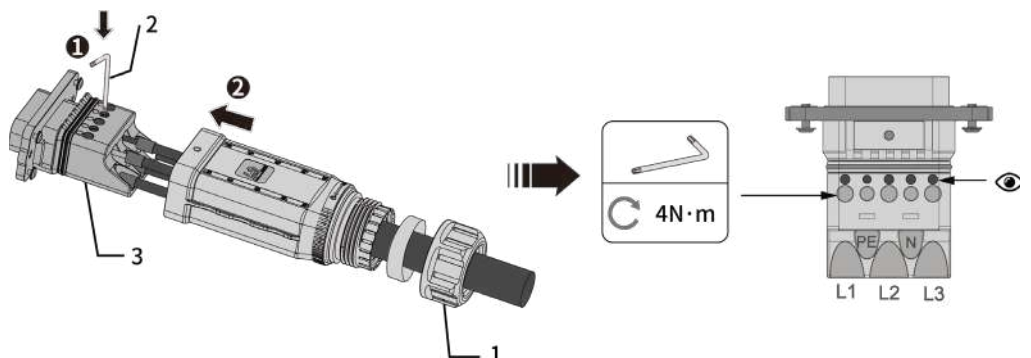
Die Kabel am Kontaktträger anschließen und die Gehäuseschrauben festziehen.
